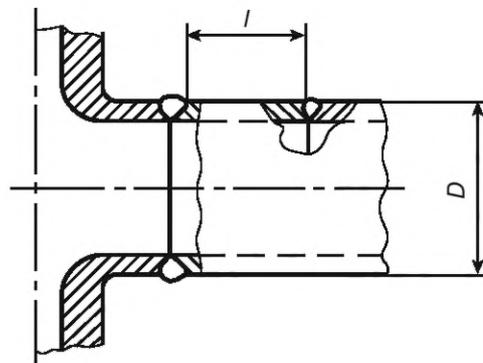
Расположение сварных соединений трубопровода с патрубком
